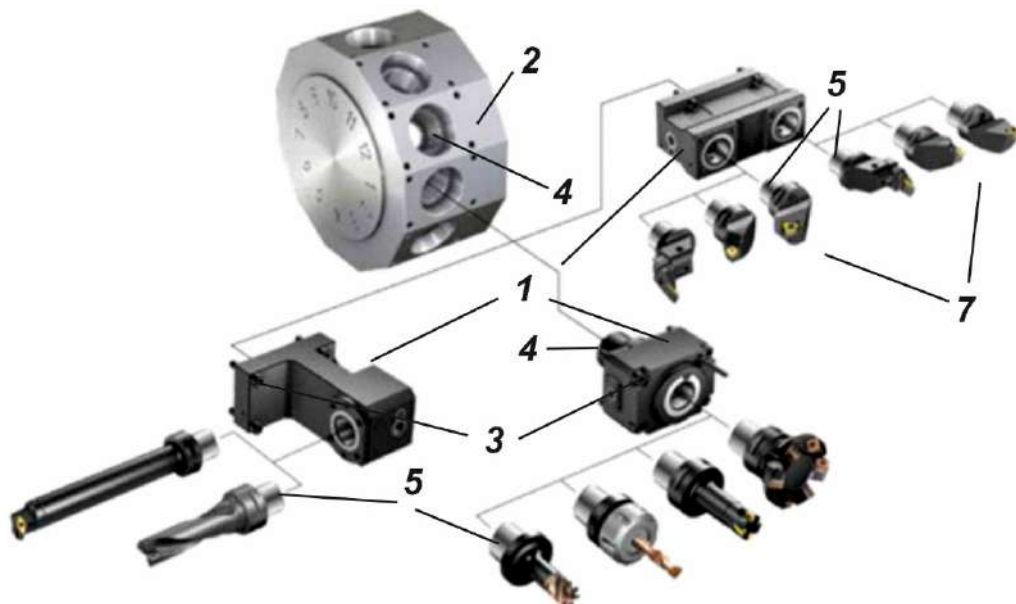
Інструментальна система токарного верстата на основі оправок Coromant Capto
